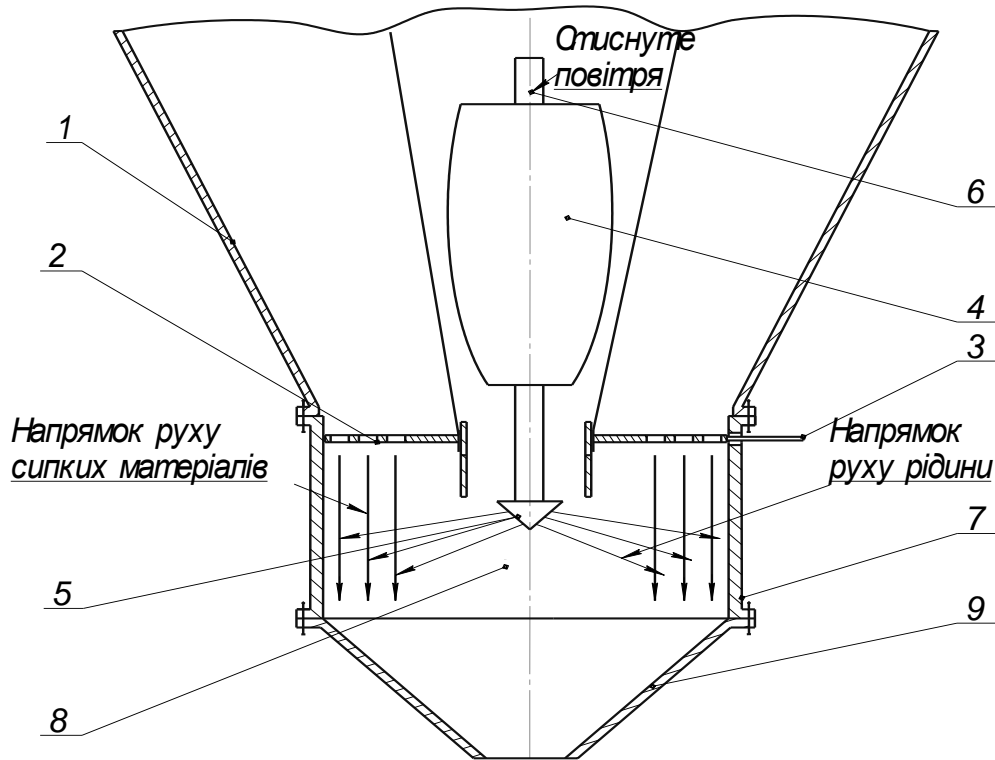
Конструктивна схема розробленого гравітаційного змішувача: 1 – бункер; 2 – дозатор вібраційно-решітний; 3 – привід дозатора; 4 – ємкість для рідини; 5 – розпилювач; 6 – патрубок стиснутого повітря; 7 – корпус; 8 – камера змішування; 9 – конус вивантажувальний
